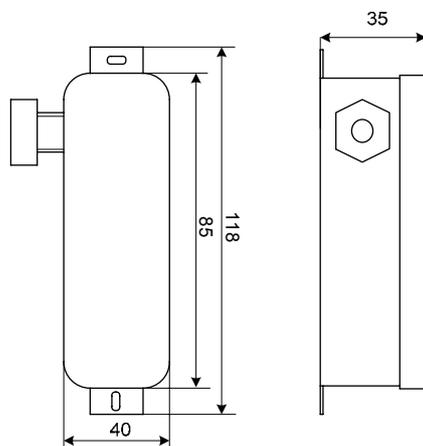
Габаритные размеры термопреобразователя сопротивления типа ДТНА-500
